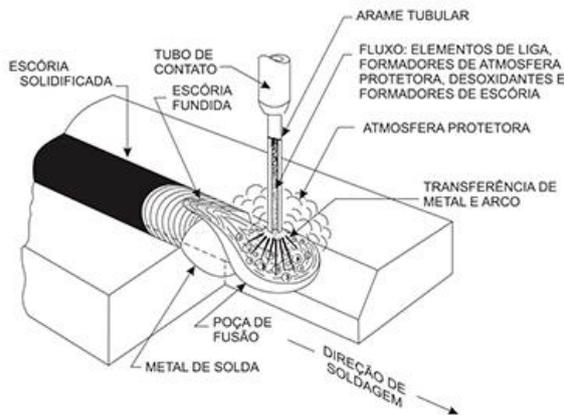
Processo de soldagem com arame auto protegido – FCAW
